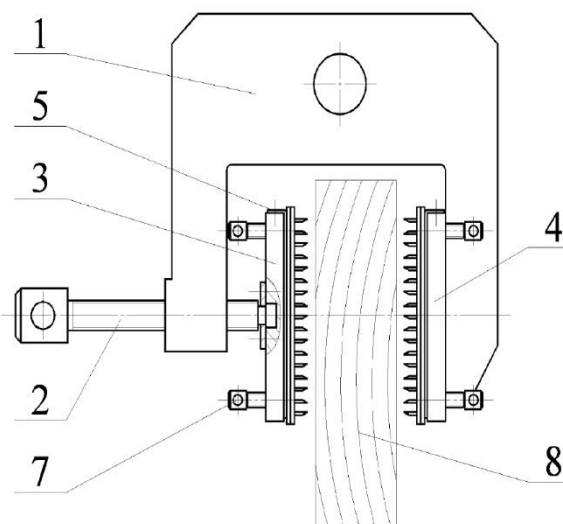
Грузозахватное устройство с ошипованными контактными элементами для перемещения деревянных конструкций: 1 – П-образный корпус; 2 – зажимной винт; 3 – подвижный контактный элемент; 4 – неподвижный контактный элемент; 5 – металлическая зубчатая пластина; 7 – отжимной винт; 8 – перемещаемая деревянная конструкция
